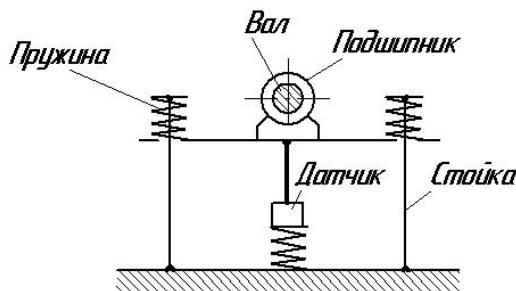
Схема связи пьезодатчика с валом стенда балансировки колес
